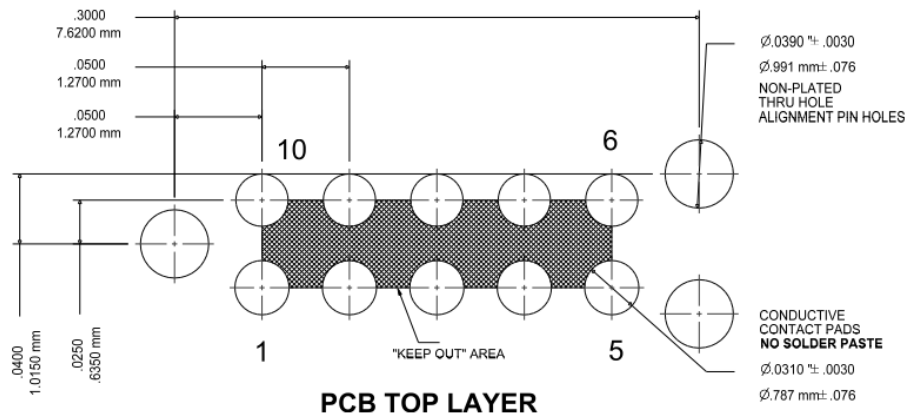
Footprint des Tag-Connect Debug-Steckers [12]
